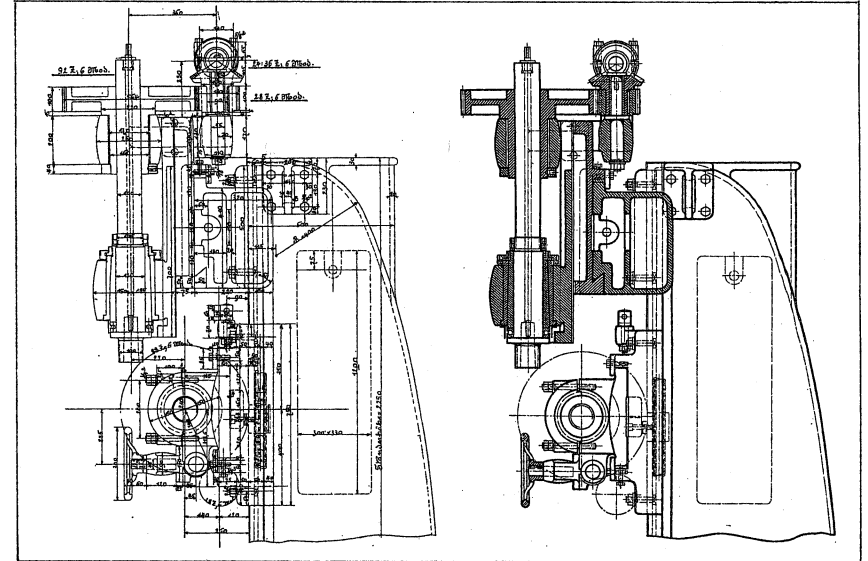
/01: Gesamtzeichnung einer Bohrmaschine mit allen Maßen und ohne Maße (um 1906)
